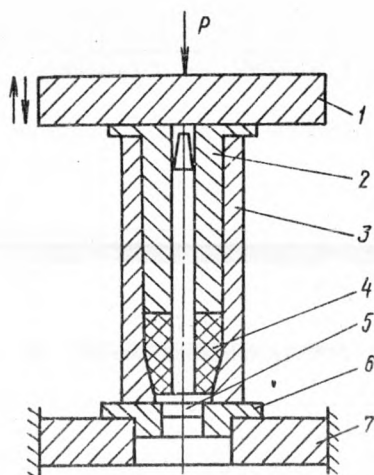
Прессформа для прессования пробок для ролевой бумаги:
